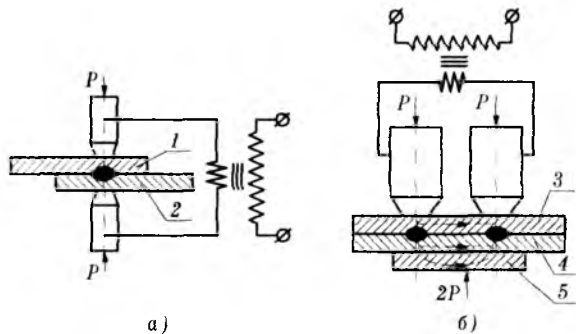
Схема двухсторонней (а) и односторонней (б) контактной точечной сварки:
